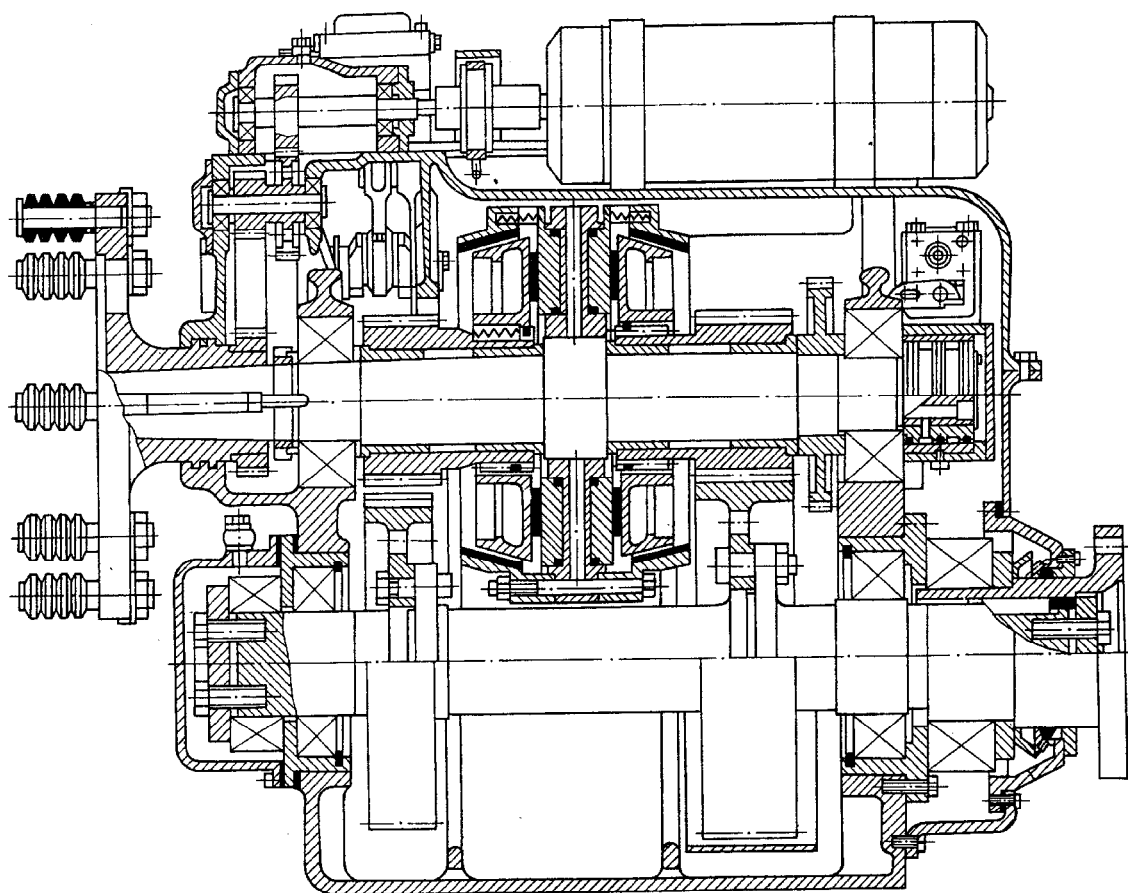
Ревёрс-редукторная передача 27РРП-230 /продольный разрез/
